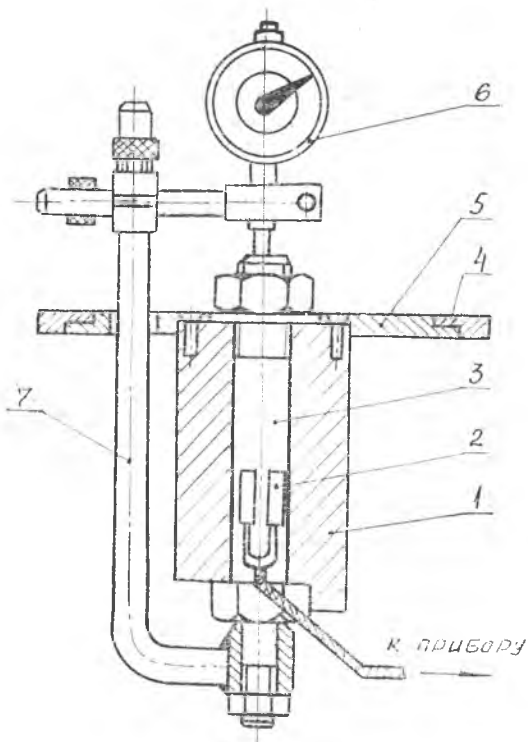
Конструкция приспособления для проведения лабораторного эксперимента
